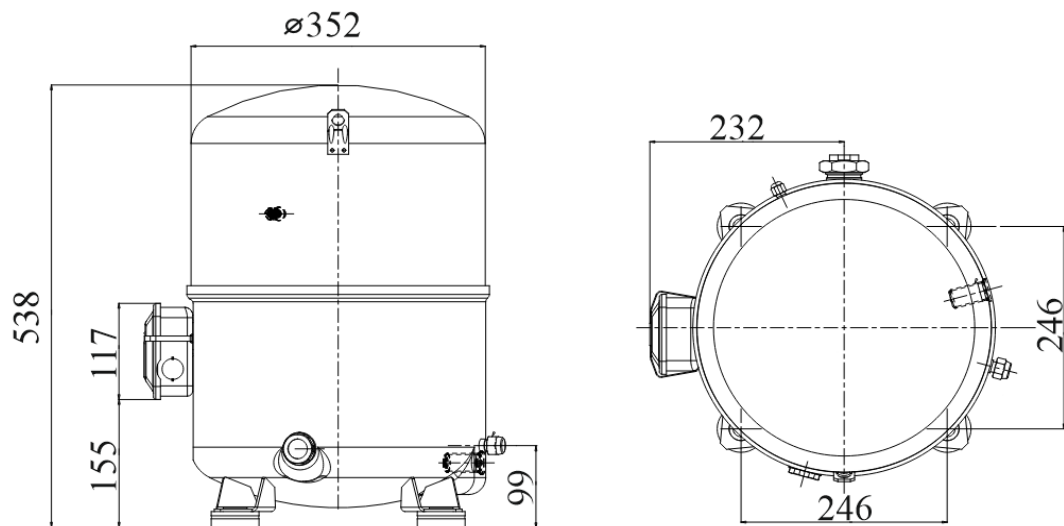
Зовнішній вид та габаритні розміри компресора MTZ100-4
